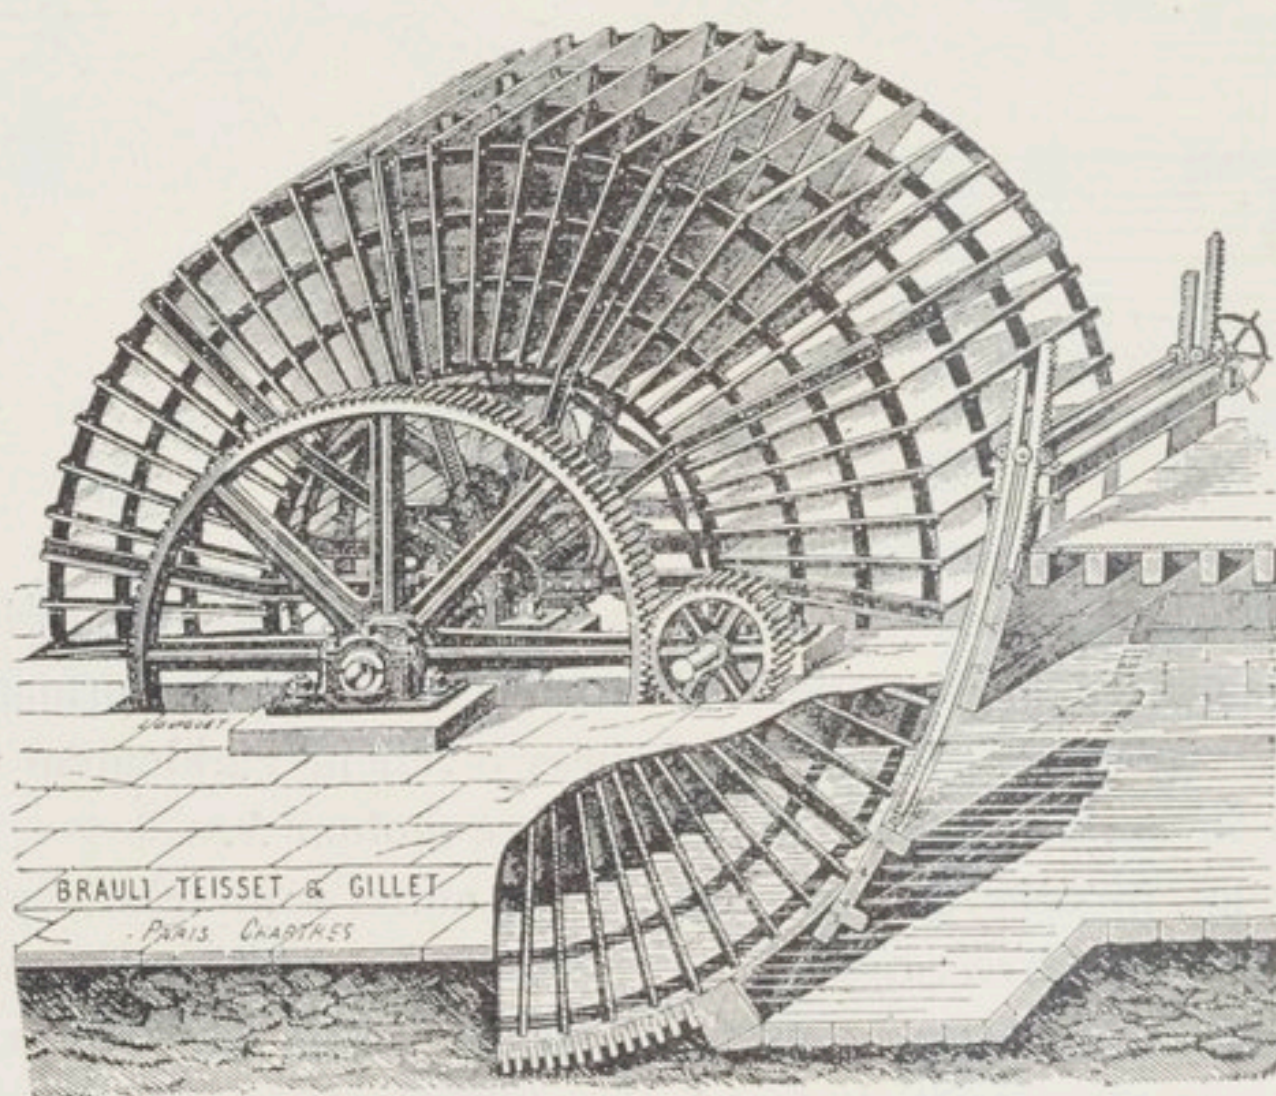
Roue de côté Sagebien. Vue d'ensemble.
